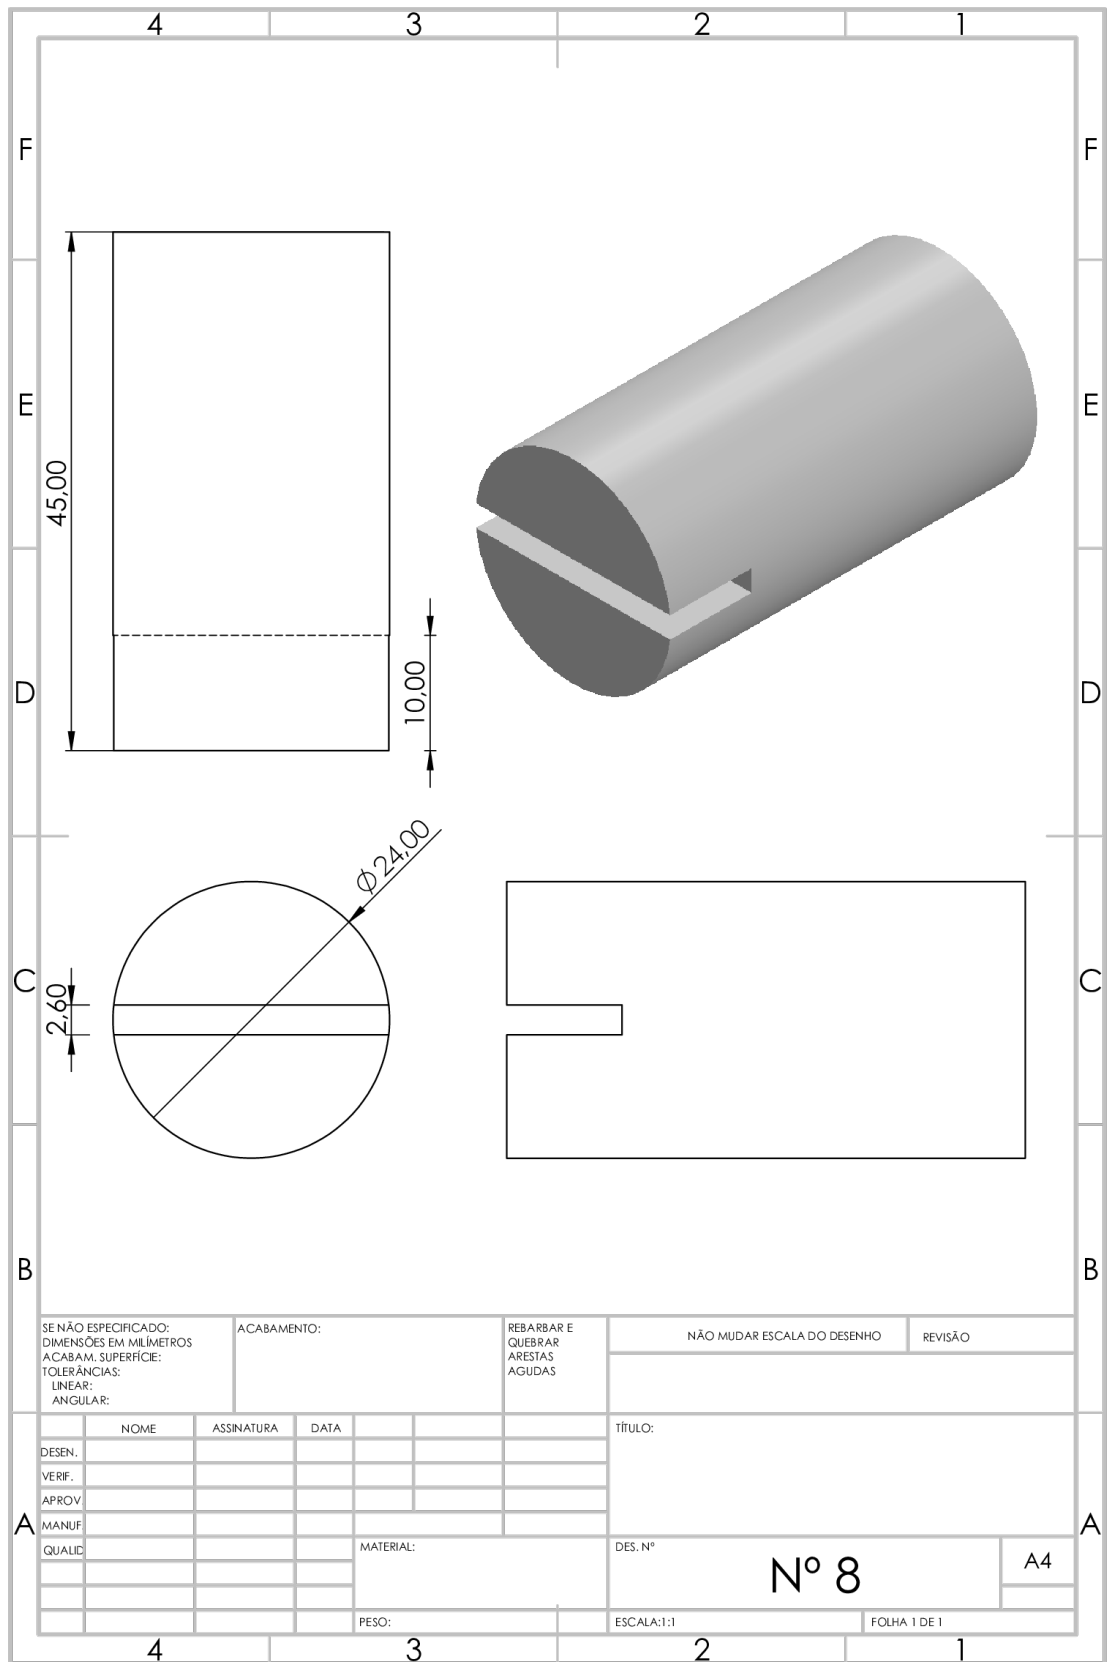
Desenho Técnico da Base do Suporte de LEDs Lateral
